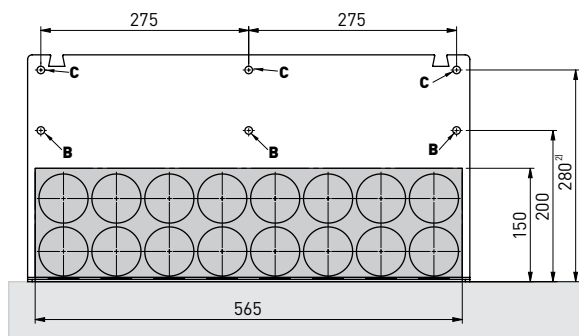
Praticare dei fori di montaggio per il passante tubo nella stiva di stoccaggio
